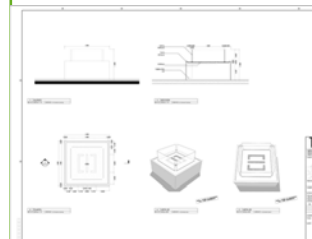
Plano enviado por el cliente donde se muestra lo requerido. de la chimenea modelo A
